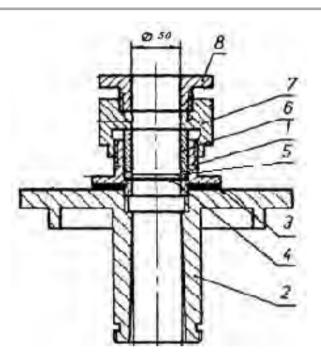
Удерживающее приспособление в разрезе: 1, 2 — корпус; 3, 5 — прокладки; 4 — фильтр; 6 — втулка; 7 — гайка; 8 — винт
